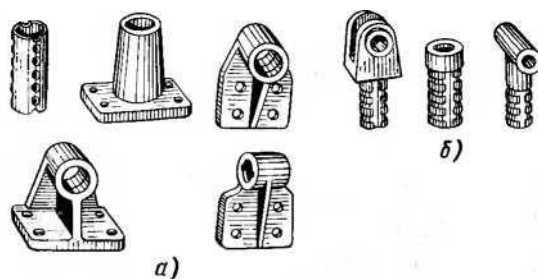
Типовые конструкции установочных элементов сборочных приспособлений:
